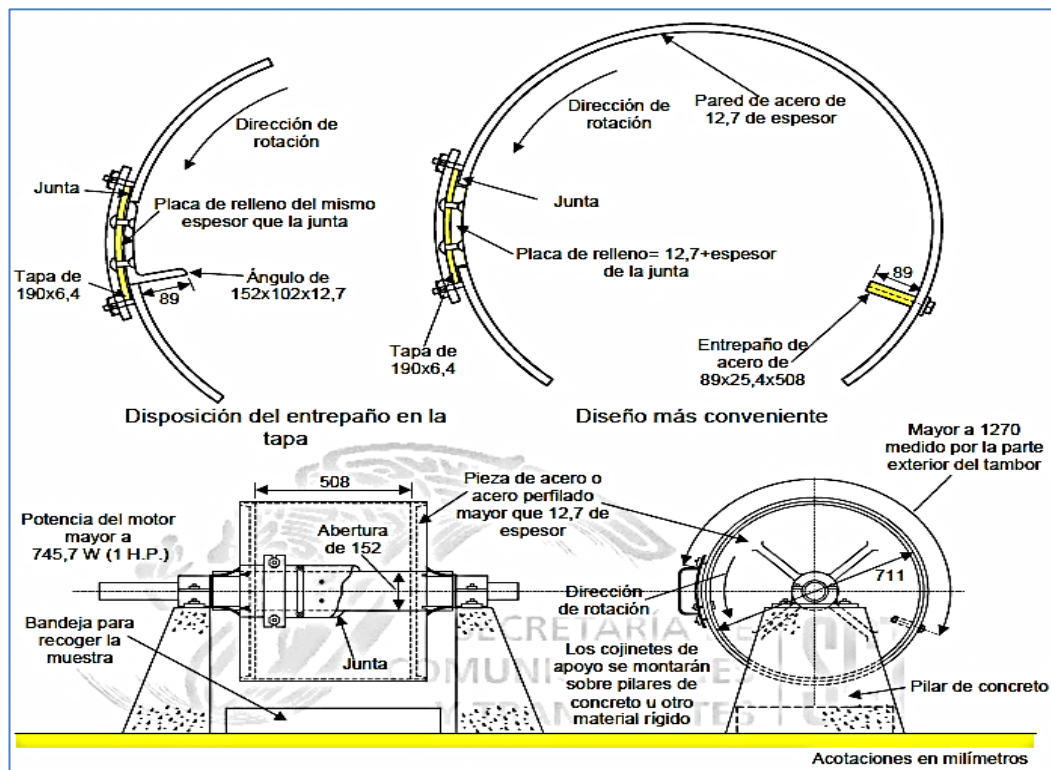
Dimensiones básicas de la Máquina de los Ángeles.
